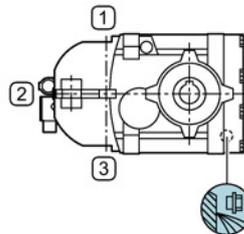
Einbautagen für Flachgetriebe FZAD und FDAD, Aufsteckausführung, Baugröße 29, 2-stufig und 3-stufig
